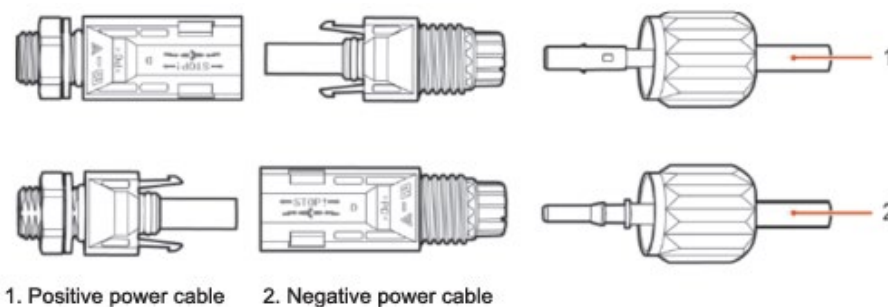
Collegamento dei cavi di alimentazione in ingresso CC (2)
